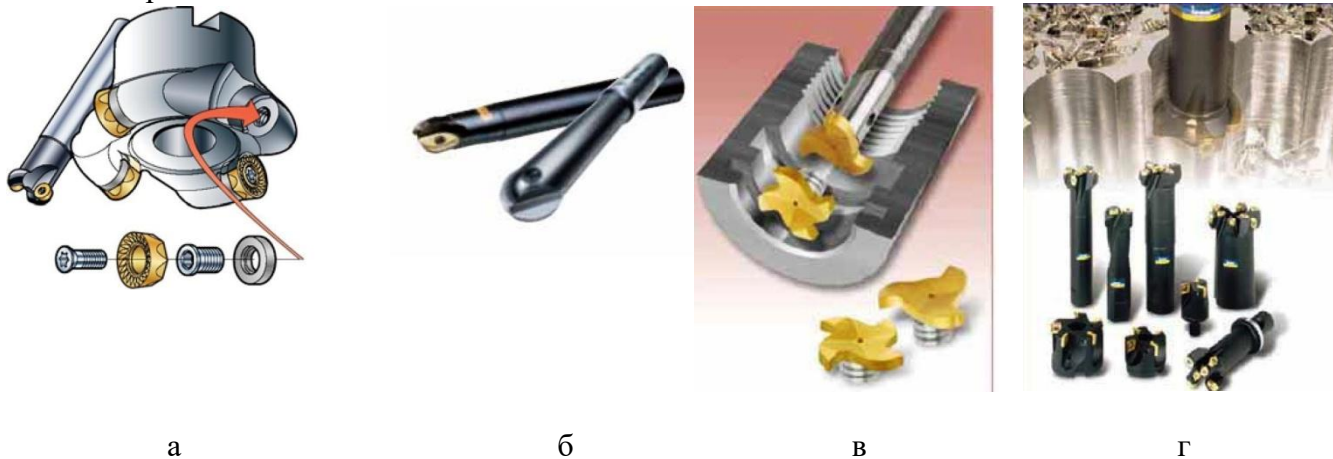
Фрези CoroMill 200 (а); CoroMill R216 і CoroMill R216F (б); закріплення інструментів невеликих діаметрів (в); плунжерні фрези (г)
